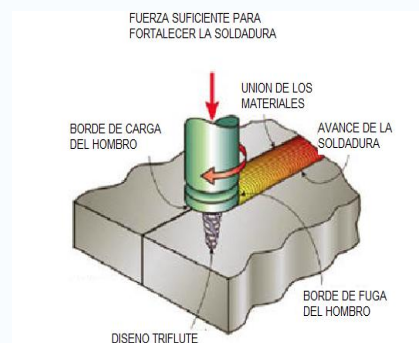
Ilustración de la herramienta FSW en proceso de soldado
